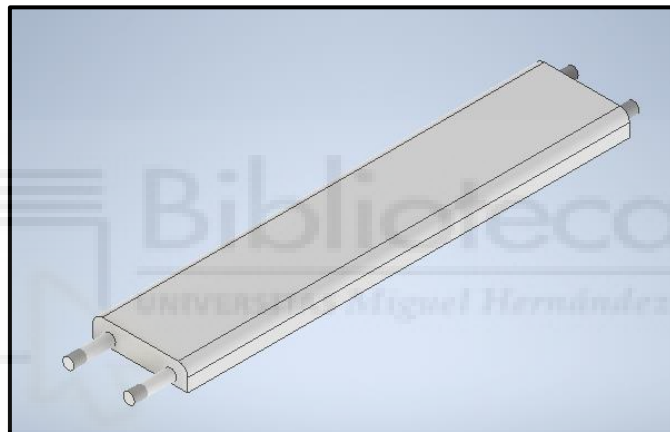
Diseño de la pieza de unión del motor del actuador con el soporte del mismo.
